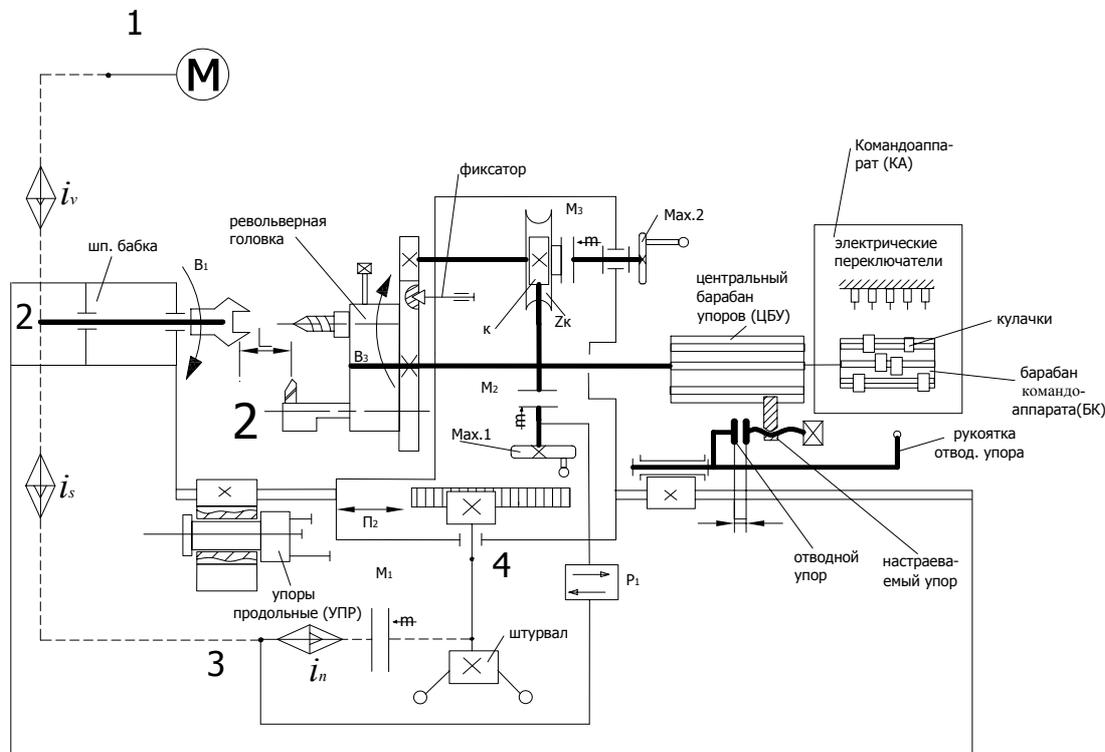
Структурная схема токарно-револьверного станка модели 1341
